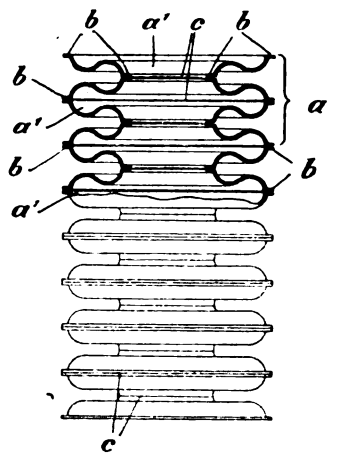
Geschweißter Schlauch aus ~-förmigen Einzelscheiben.
